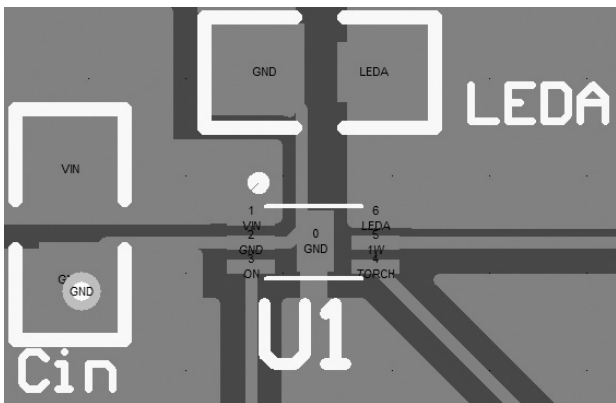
UTDFN-1.5x2-6L 的 PCB 布线图
